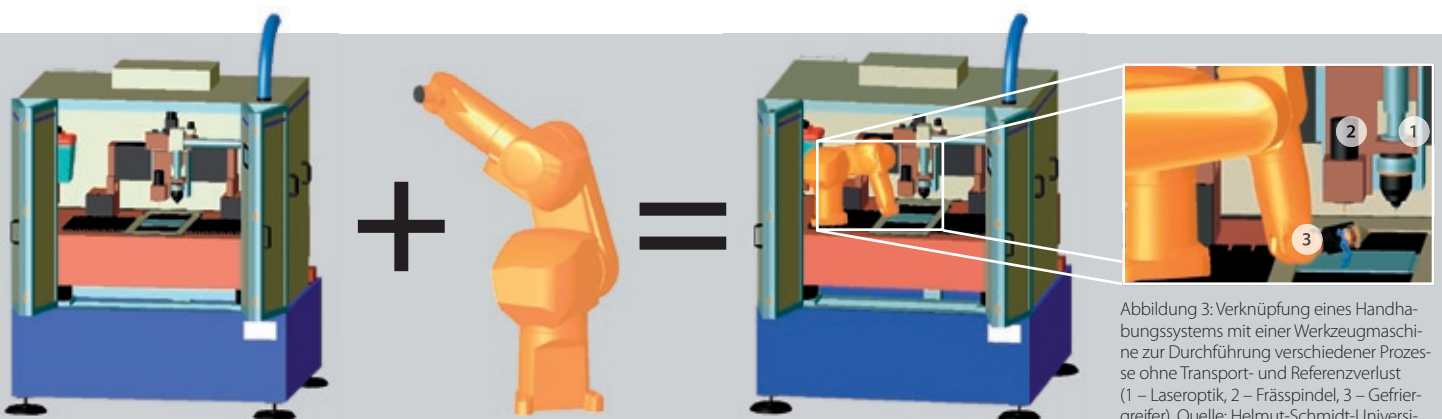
Verknüpfung eines Handhabungssystems mit einer Werkzeugmaschine zur Durchführung verschiedener Prozesse ohne Transport- und Referenzverlust (1 – Laseroptik, 2 – Frässpindel, 3 – Greifgreifer). Quelle: Helmut-Schmidt-Universität, Universität der Bundeswehr Hamburg.
